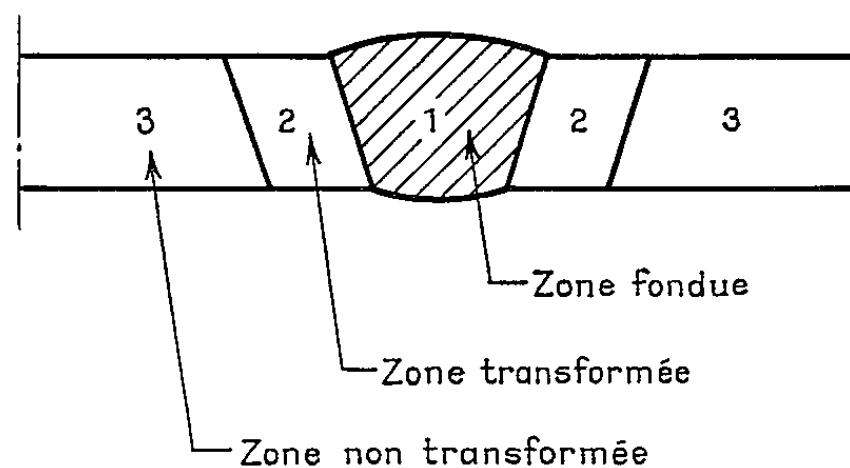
Position des différentes zones dans une plaque soudée.
